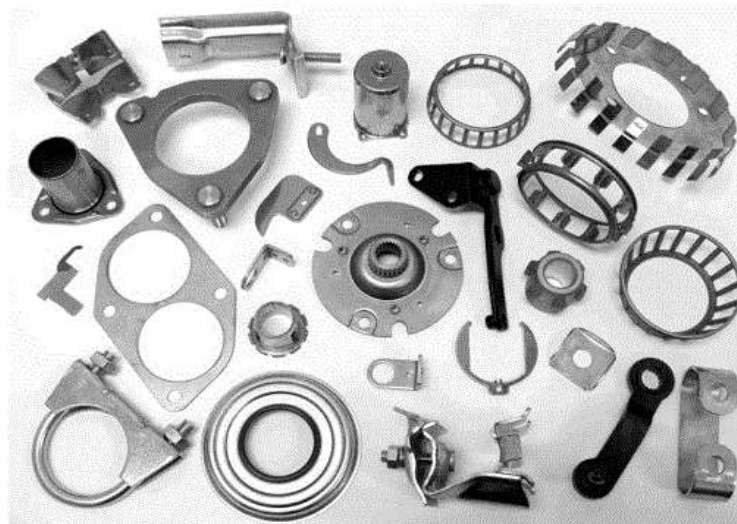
Штамповані і ковані заготовки (штамповки і поковки)
